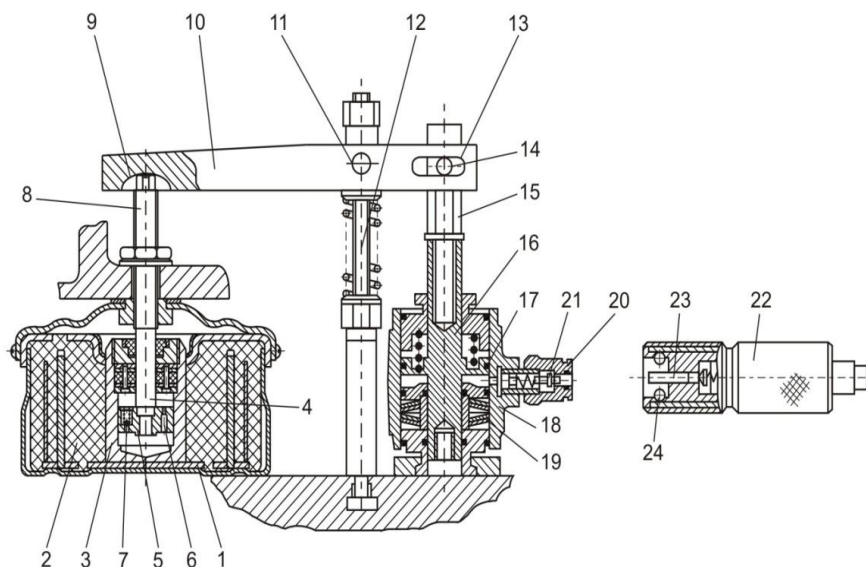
Общий вид виброизолирующего устройства: 1 – основание; 2 – резиновый элемент; 3 – цилиндр; 4 – шток; 5 – поршень; 6 – калиброванное отверстие; 7 – клапан сжатия; 8 – регулировочный винт; 9 – сферическая поверхность лунки; 10 – прихват; 11 – ось; 12 – стойка; 13 – продольный паз; 14 – ось; 15 – опора; 16 – опорный шток; 17 – поршень; 18 – гидроцилиндр; 19 – пружинный аккумулятор; 20 – малая полумуфта; 21 – клапан; 22 – большая полумуфта; 23 – клапанный штырь; 24 – шарики
